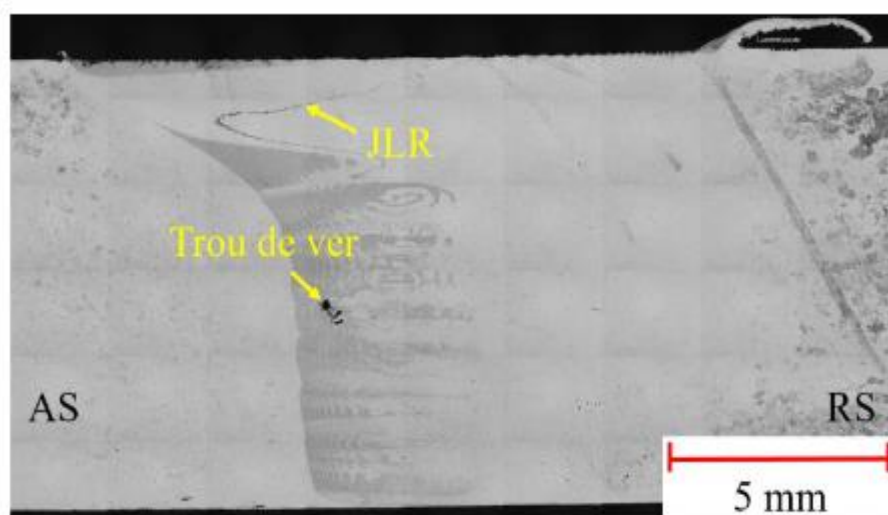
Macrographie d'une soudure en 6061-T6 de 9,5 mm [14]
